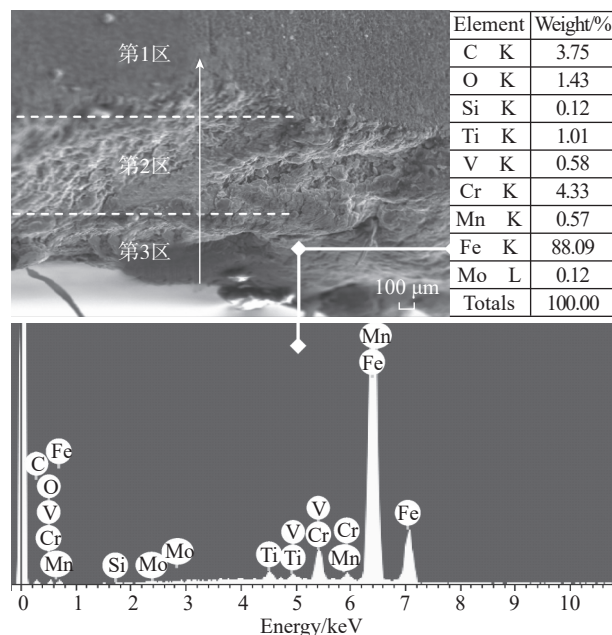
PCBN 刀具前刀面磨损微观结构和 EDS^[9]
